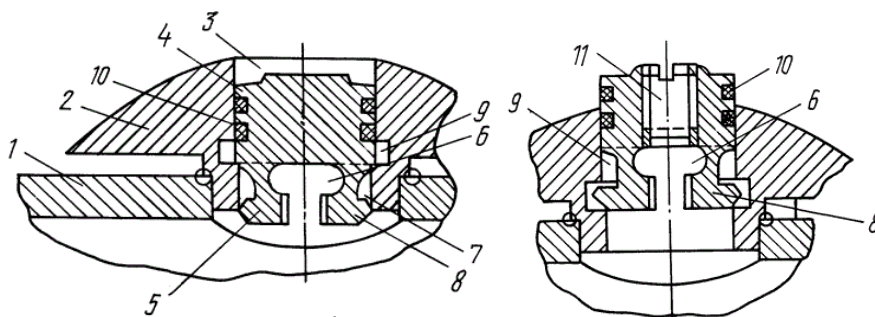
Центратор гидравлический: 1 – обсадная труба; 2 – корпус; 3 – цилиндрический канал; 4 – центрирующий орган; 5 – сегментообразные элементы; 6 – овальная полость; 7 – кольцеобразная выемка;
